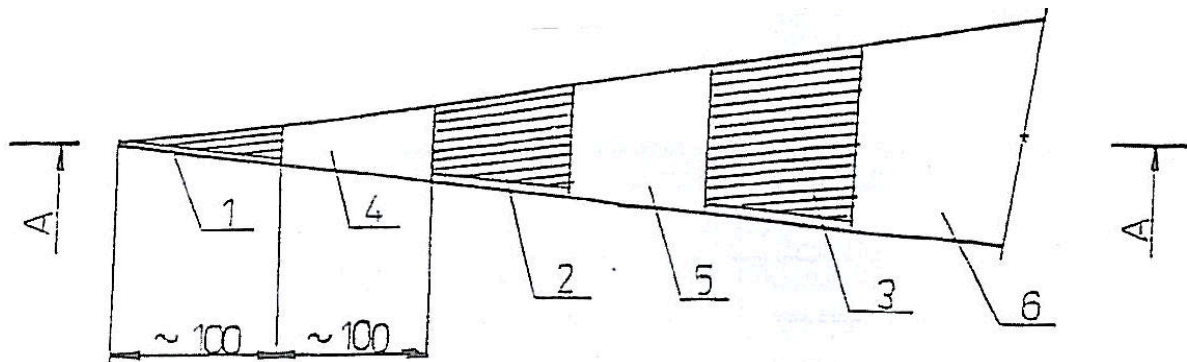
Oprava místní vady – postup kladení housenek v podélném řezu
